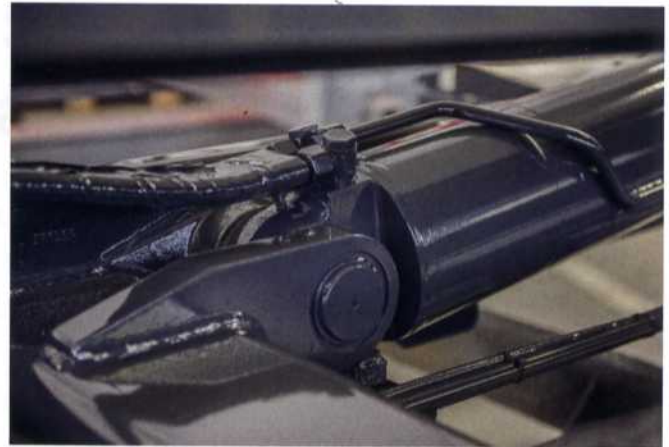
Zylinderaugen werden am Hydraulikzylinders aufgeschweißt und bilden mit einer Öse die bewegliche Verbindung des Zylinders zum LKW-Aufbau
